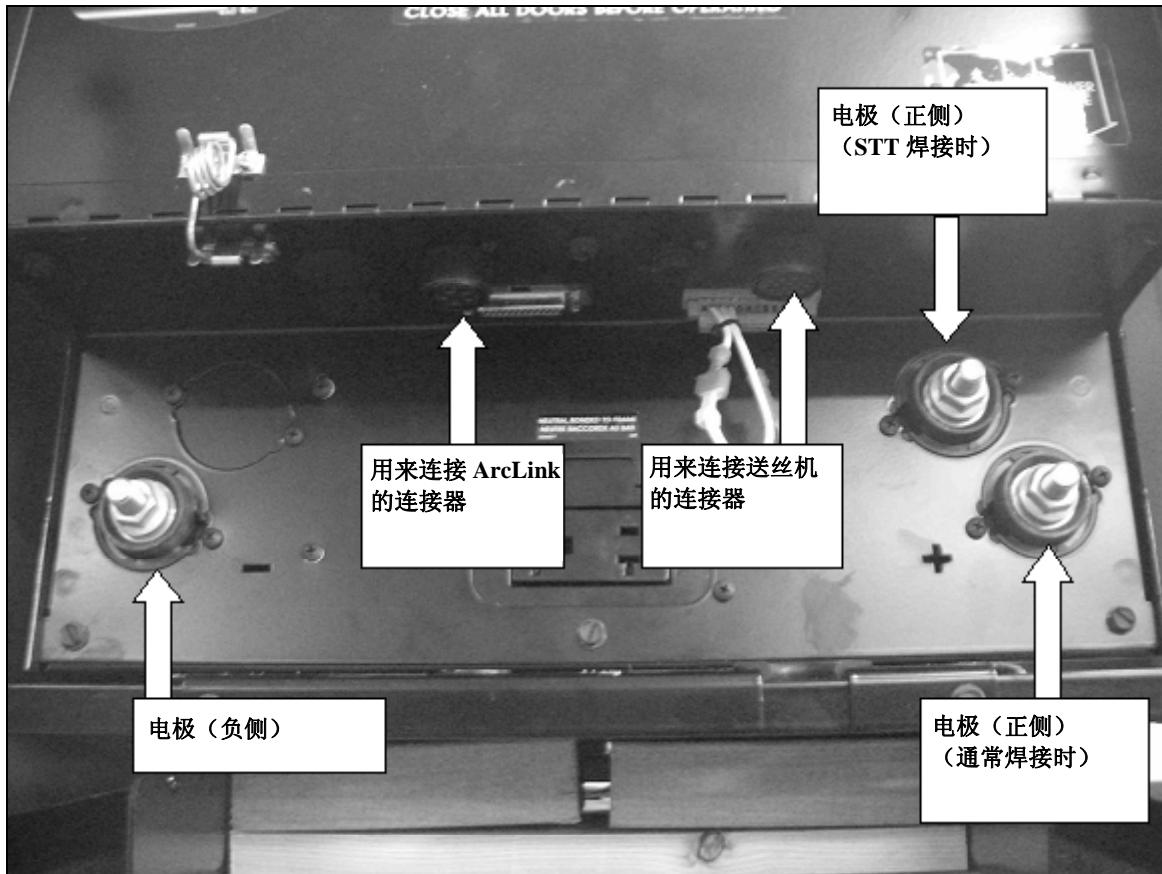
(c) ROBOWELD iC/H2 用焊接电源装置 (Power Wave 455M/STT) 的连接接口
